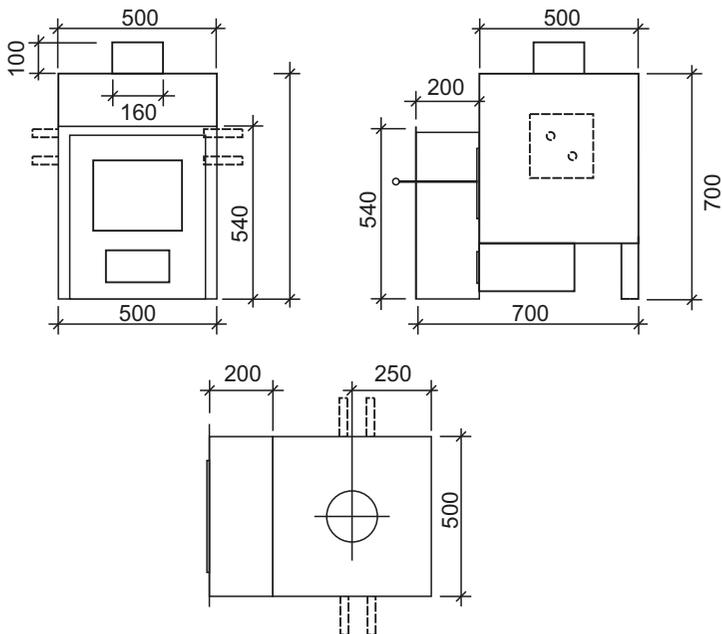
а Габаритные размеры печи «Тройка» 07-ГТ20
